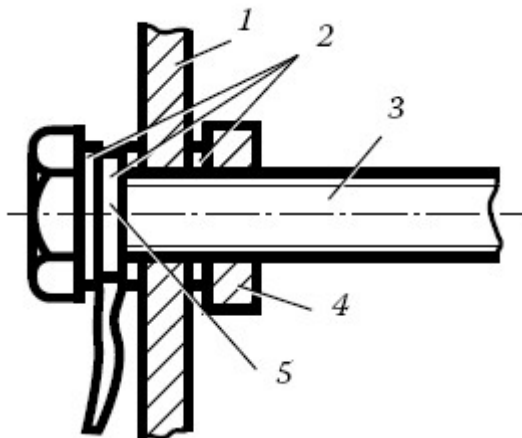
Крепление выводов сварочной обмотки:
